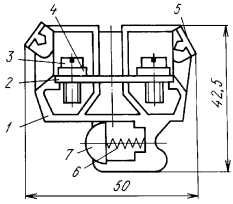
Габаритные, установочные и присоединительные размеры мостиковых зажимов
